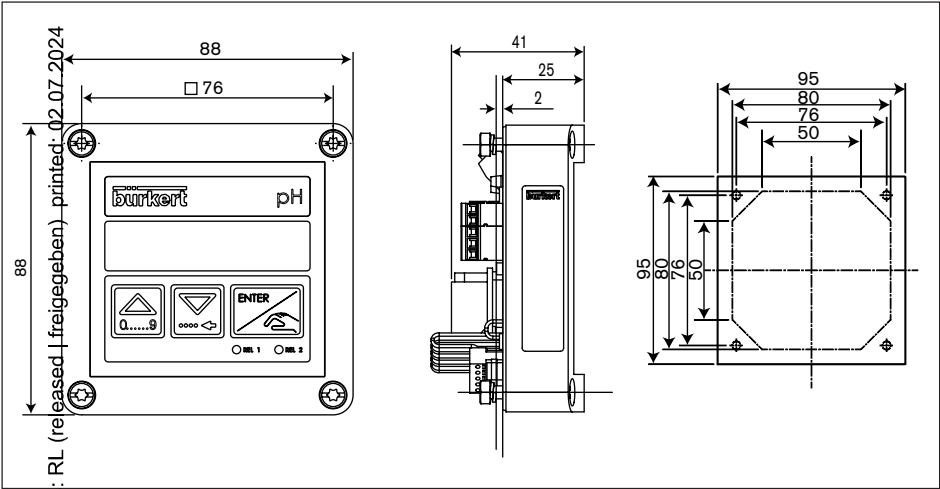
Dimensions du régulateur de pH 8205 encastrable et du plan de découpe
